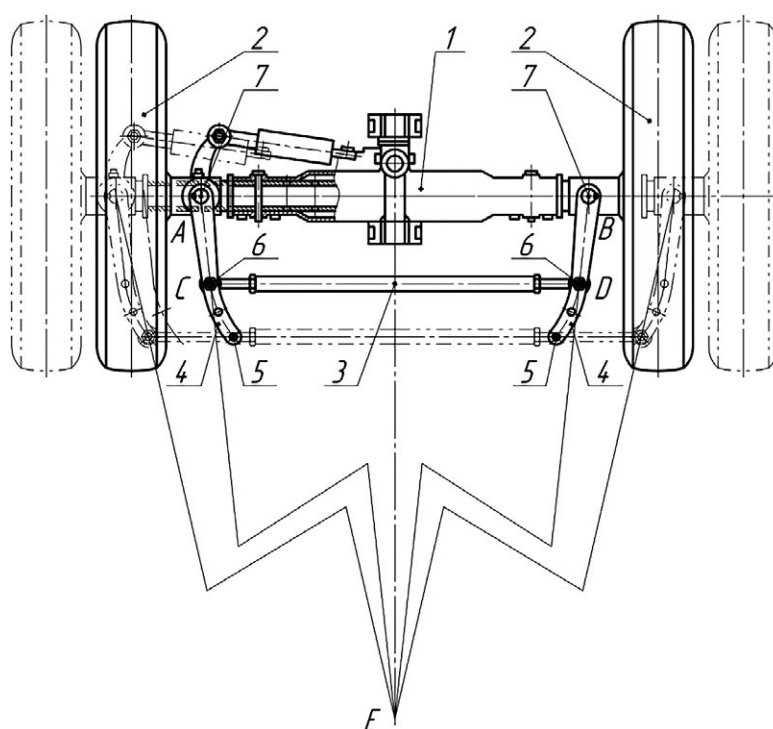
Рулевая трапеция колесной машины с изменяемой колеёй: 1 — управляемый мост; 2 — поворотные колёса; 3 — поперечная рулевая тяга регулируемой длины; 4 — поворотные рычаги; 5 — отверстия для крепления шарниров; 6 — шарниры; 7 — шкворни.
